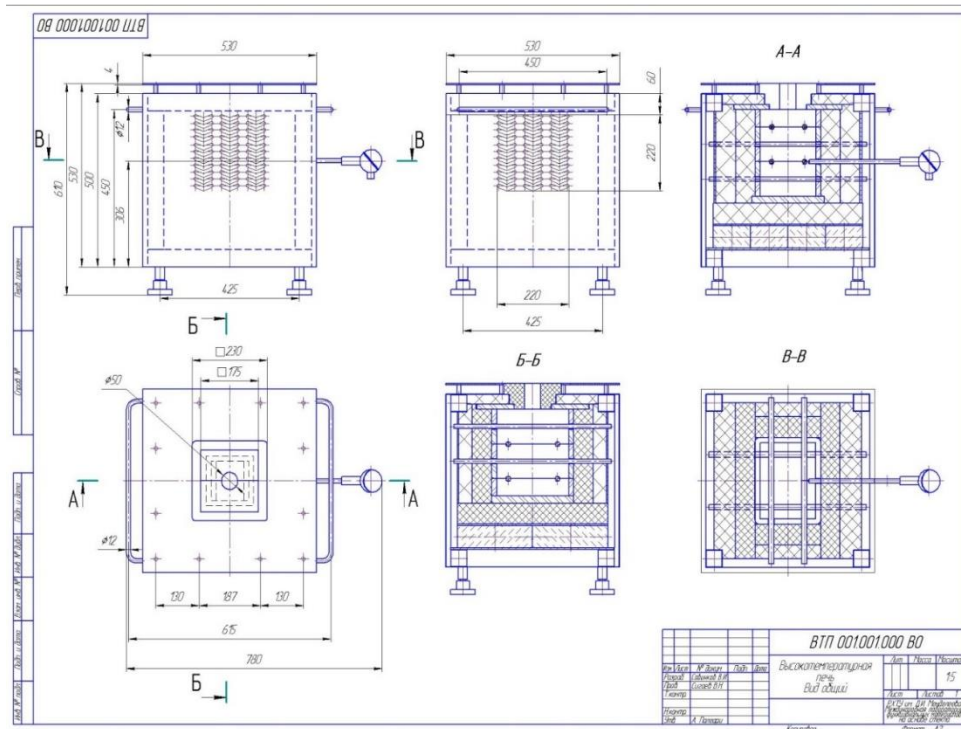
Эскиз лабораторной печи для варки стекла
